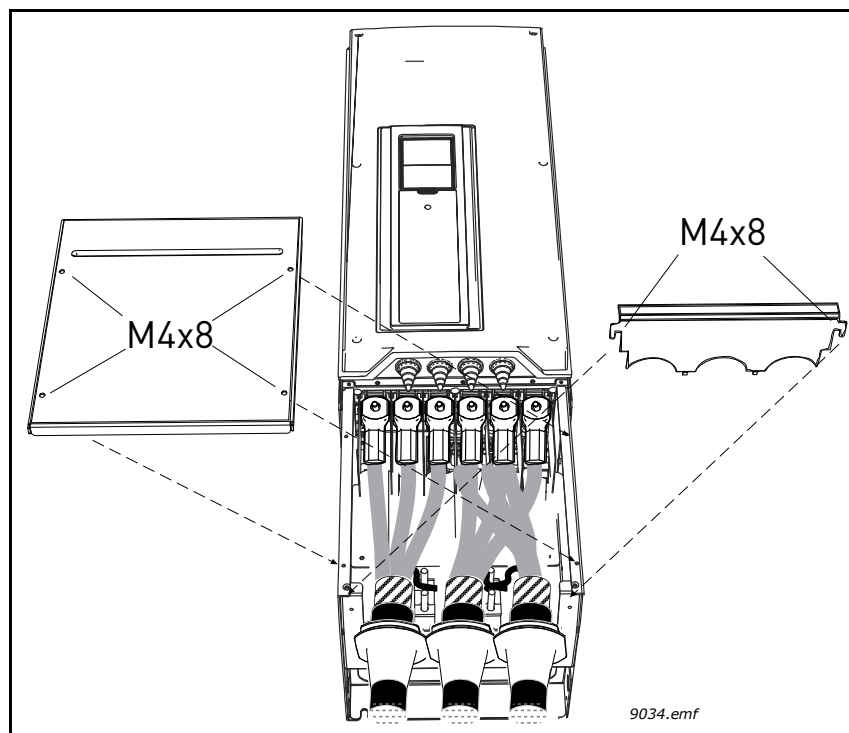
Recolocación de la placa de fijación de cables y la tapa
